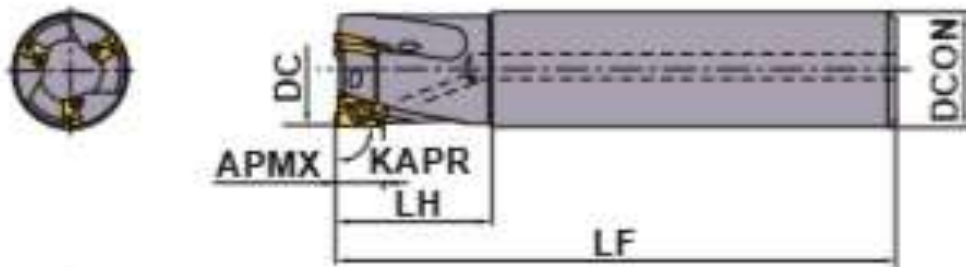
Корпус фрезы Mitsubishi для глубокого фрезерования
